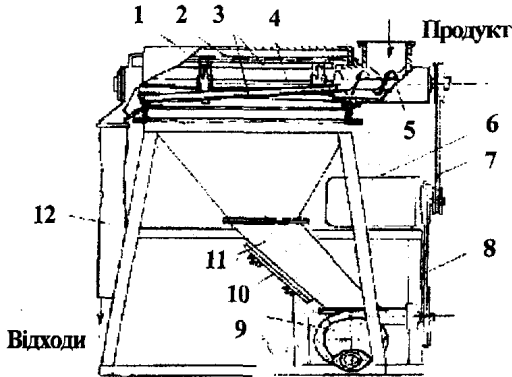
Відцентрове сито: 1 – корпус; 2 – ситовий барабан; 3 – планки; 4 – вал; 5 – шнек; 6 – електродвигун; 7, 8 – пасові передачі; 9 – шлюзовий живильник; 10 – магніти; 11 – жолоб; 12 – збірник
